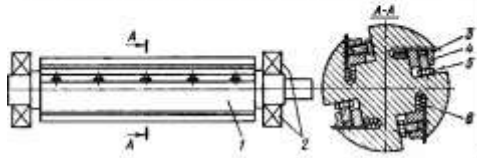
Ножевой вал фуговального станка СФК6-1: 1 — корпус, 2 — подшипники, 3 — нож, 4 — прижимный клин, 5 — винт, 6 — пружина
